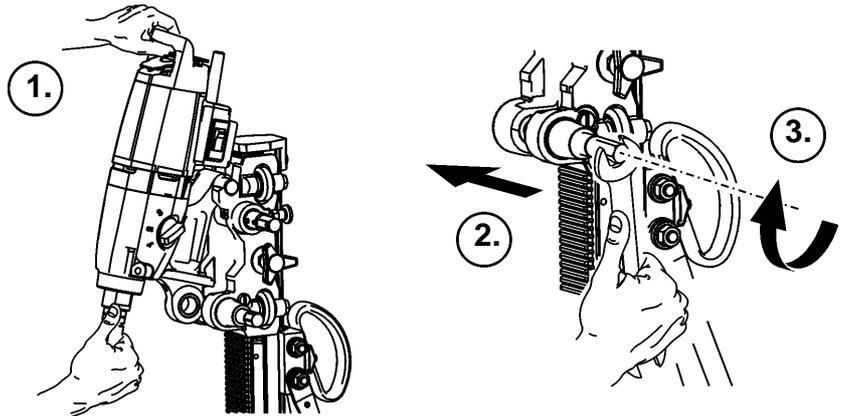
Modul-Drill-Befestigungsprinzip
